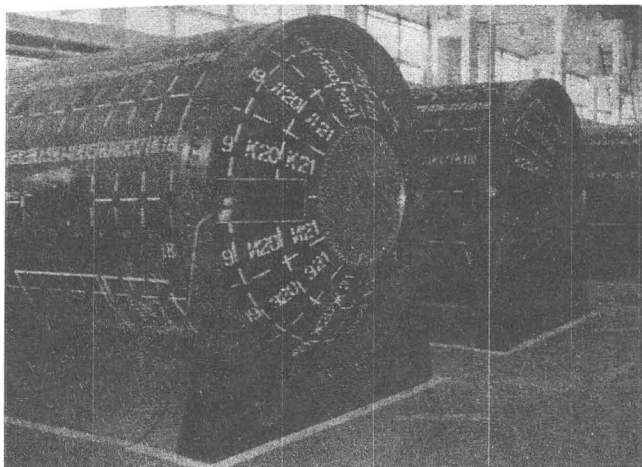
Снаряженный корпус твердотопливного ракетного двигателя первой ступени РС-22
